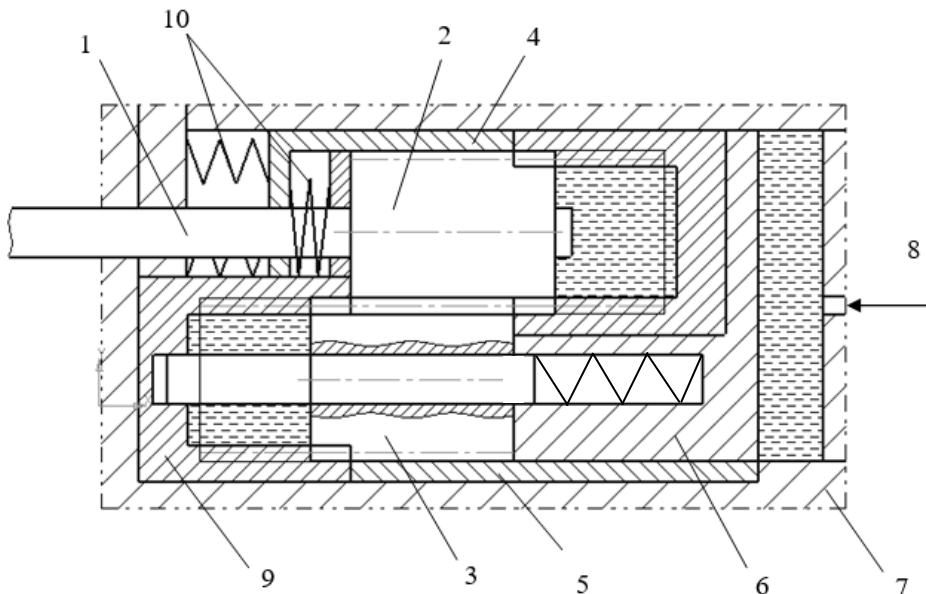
Схема механізму регулювання робочого об'єму шестеренного насосу
